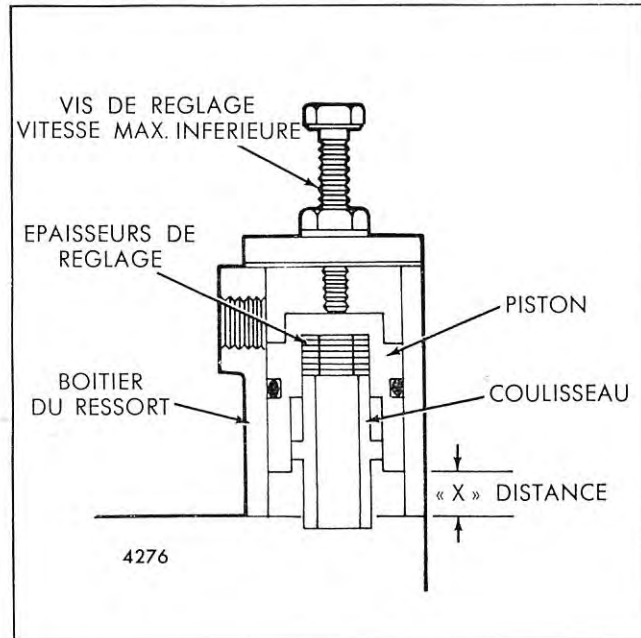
B - Régulateur à double rang de vitesses. B : modèle actuel
